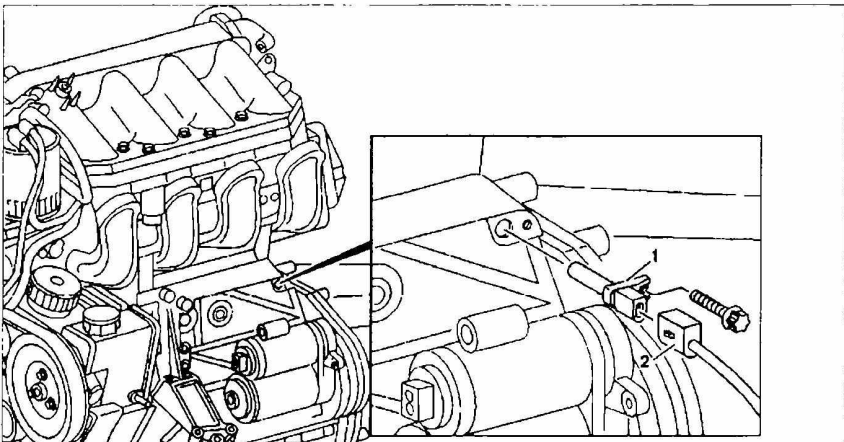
Снятие и установка датчика положения коленчатого вала:
